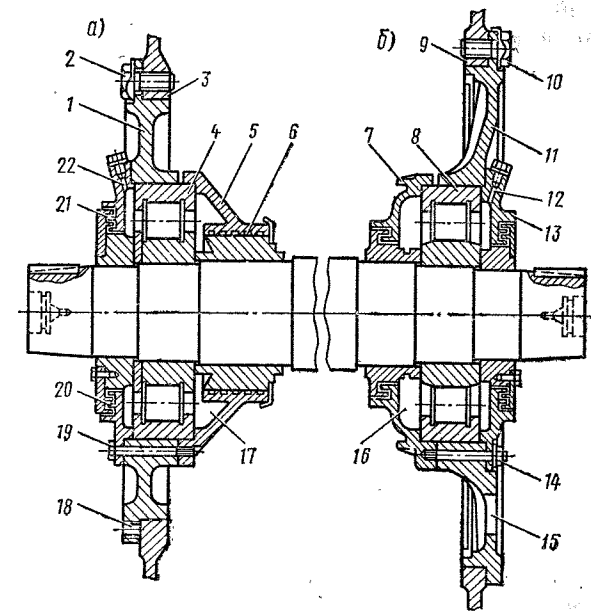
Подшипниковые щиты тягового двигателя со стороны коллектора (а) и противоположной стороны (б)
